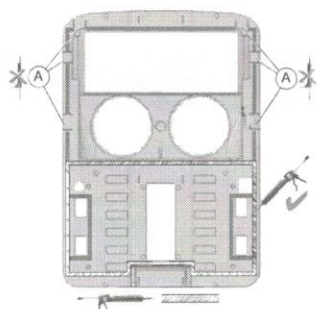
Sikaflex przy zakrzywieniu dachu równym 5200 mm
